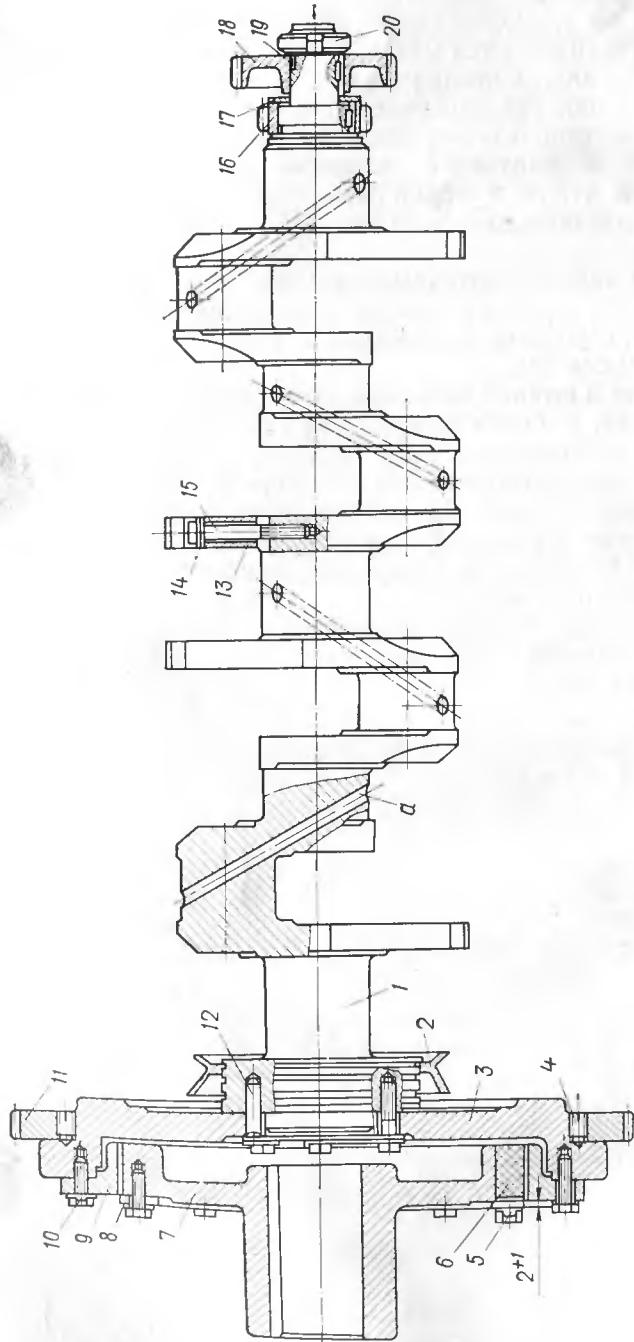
Коленчатый вал с маховиком и полумуфтами:
